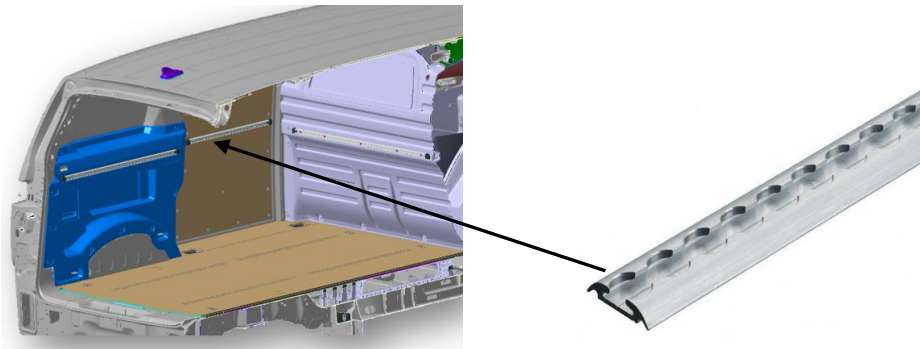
rails ZSB cloison (rails d'arrimage sur la cloison et les pièces latérales)
